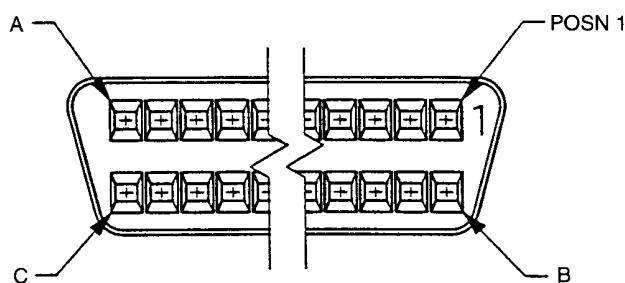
Face d'accouplement d'un connecteur avec contacts femelles
